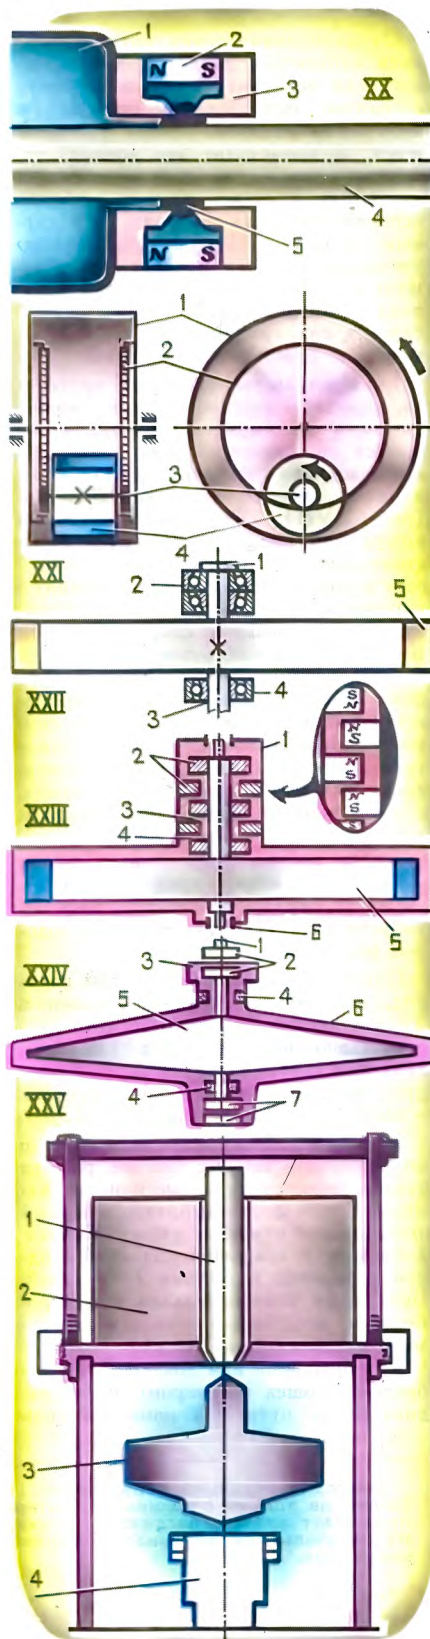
Рис. XXII. Обычная подвеска маховика (1 — упор, 2 — радиально-упорные подшипники, 3 — посадка скольжения, 4 — радиальный подшипник, 5 — маховик).
